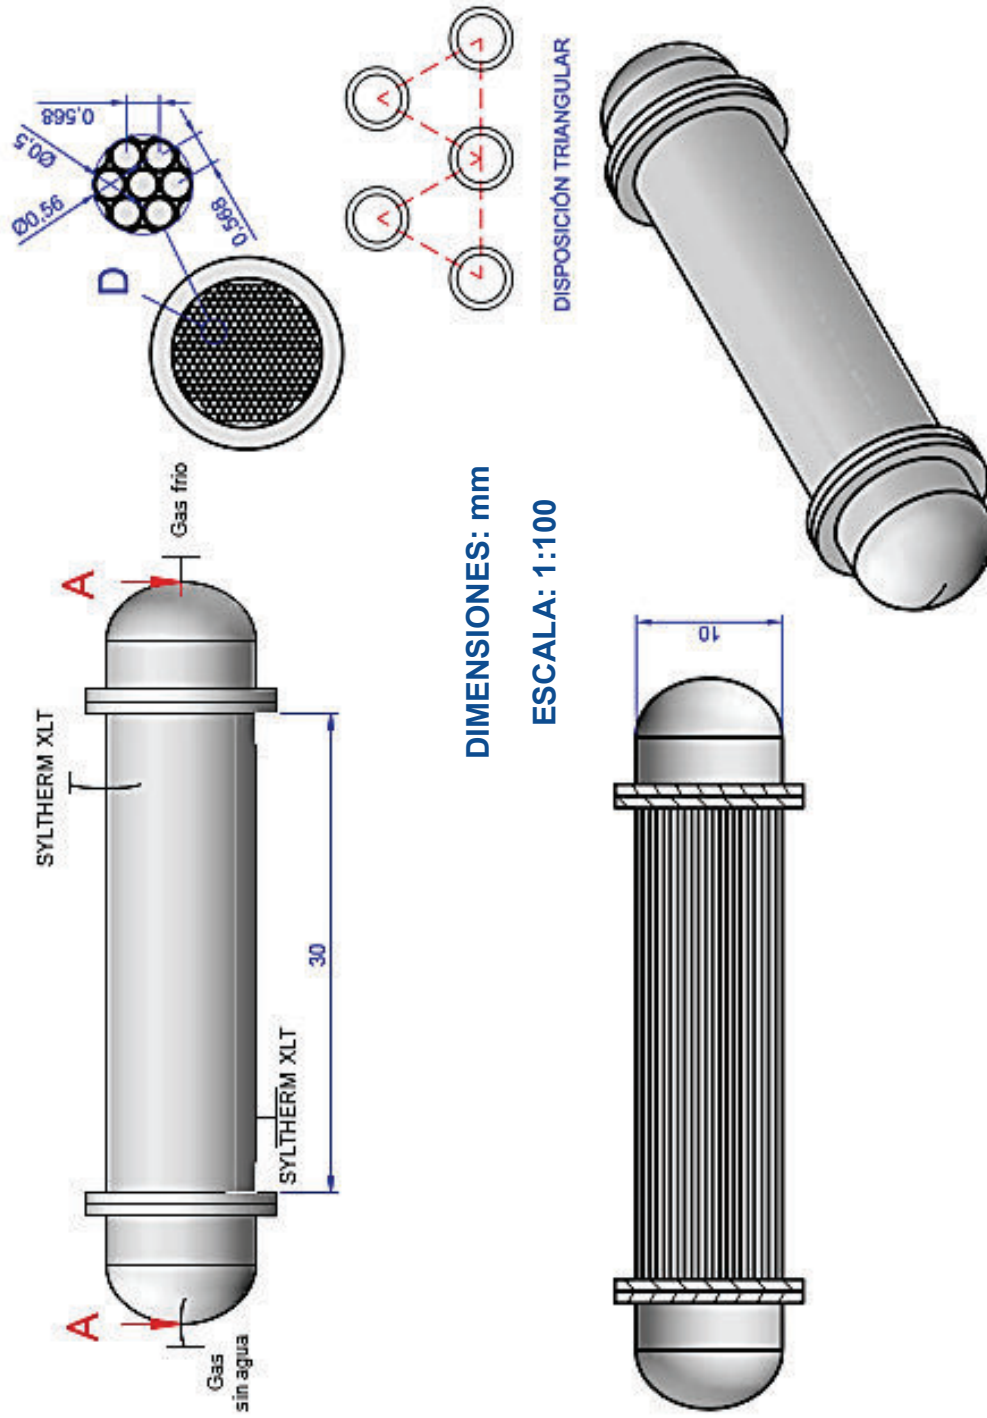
Dimensiones del intercambiador de calor 3 de tubos y coraza (E-405)
